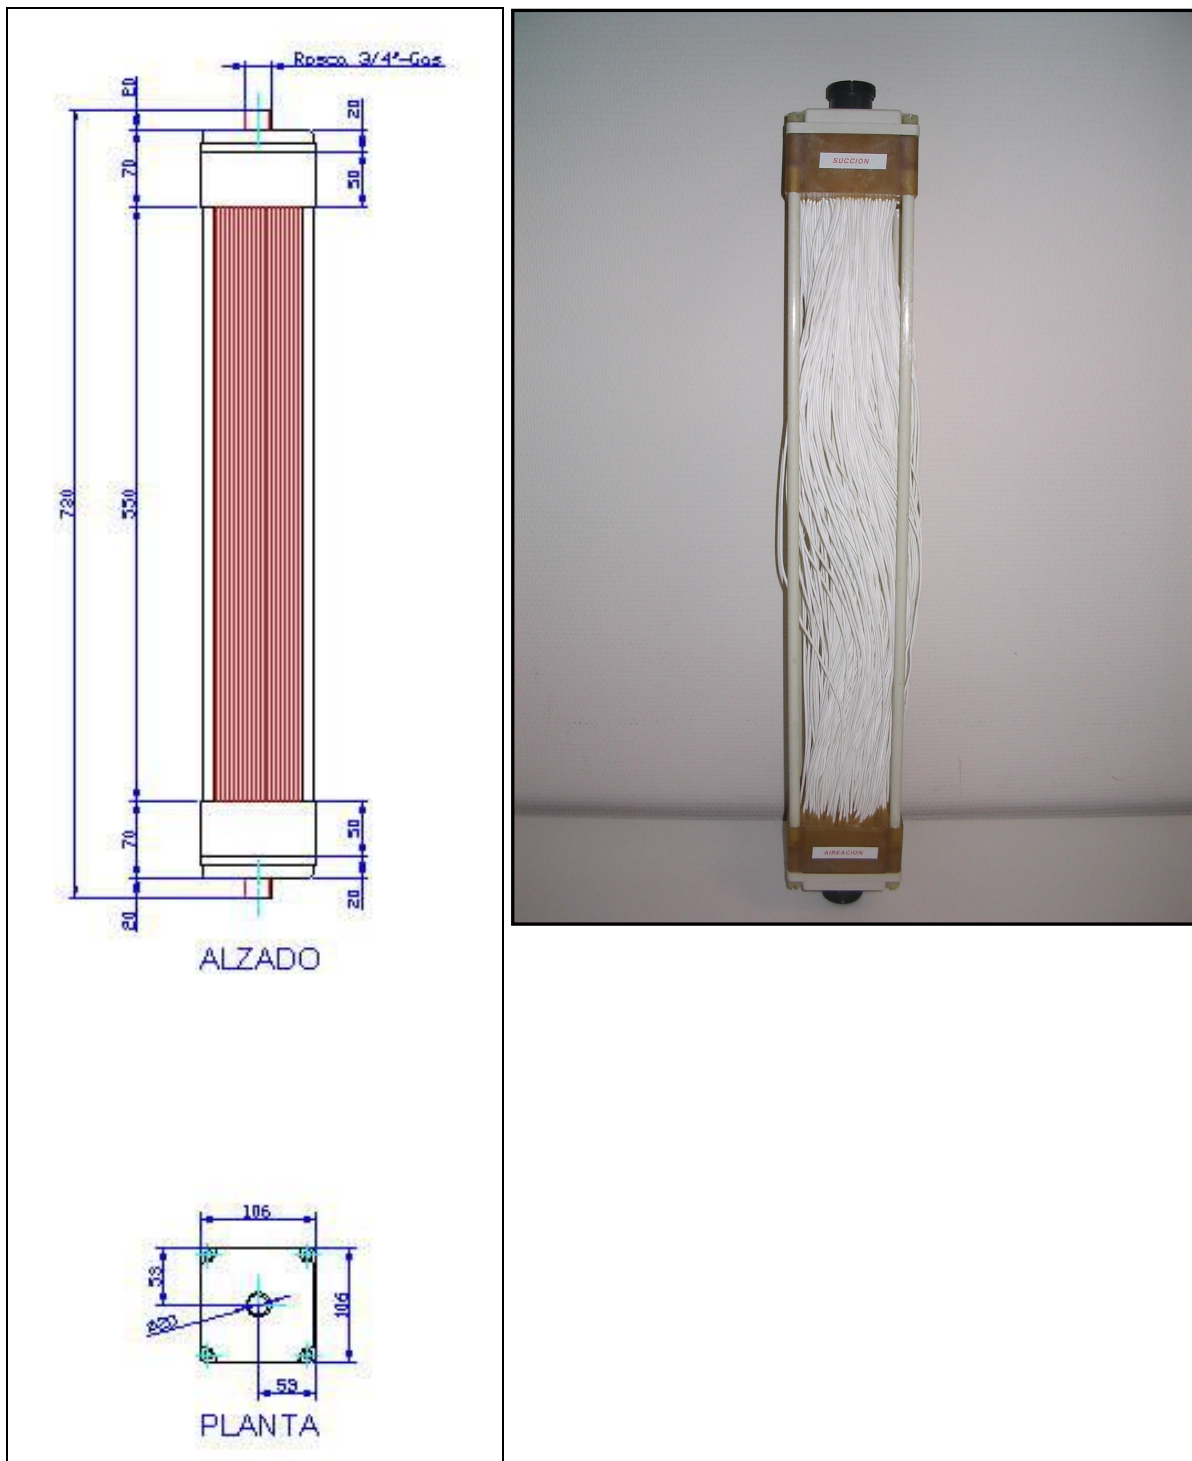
Dimensiones (mm) e imagen del módulo piloto de fibras huecas
